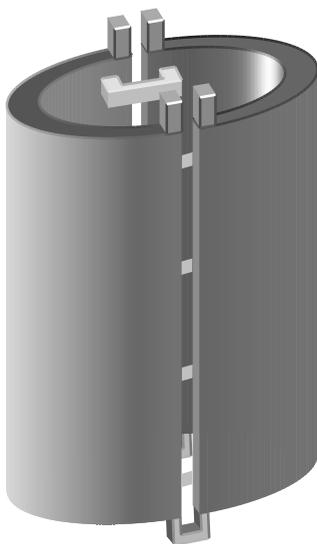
Сборка деталей толстостенного сосуда для электрошлаковой сварки продольного шва
